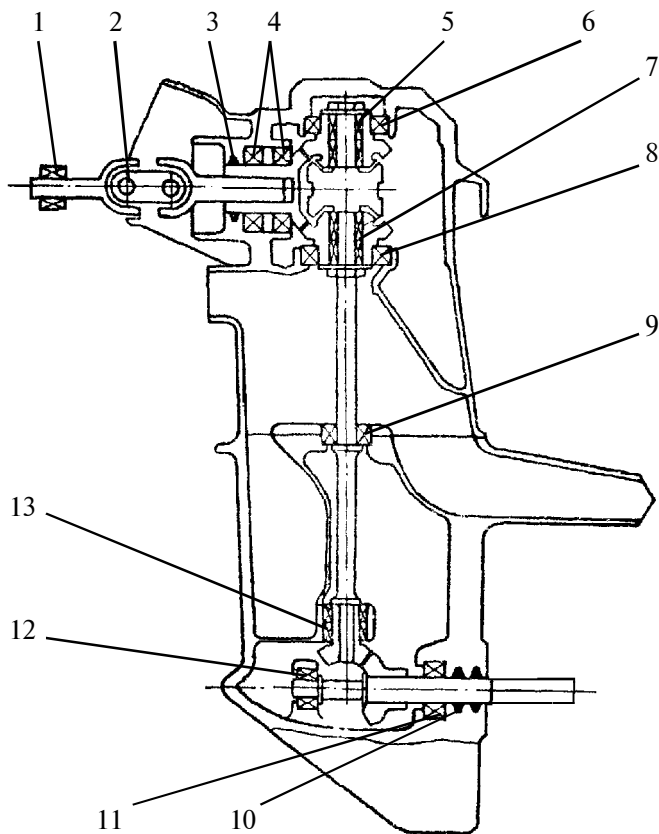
Схема расположения подшипников качения и уплотнительных манжет в колонке
